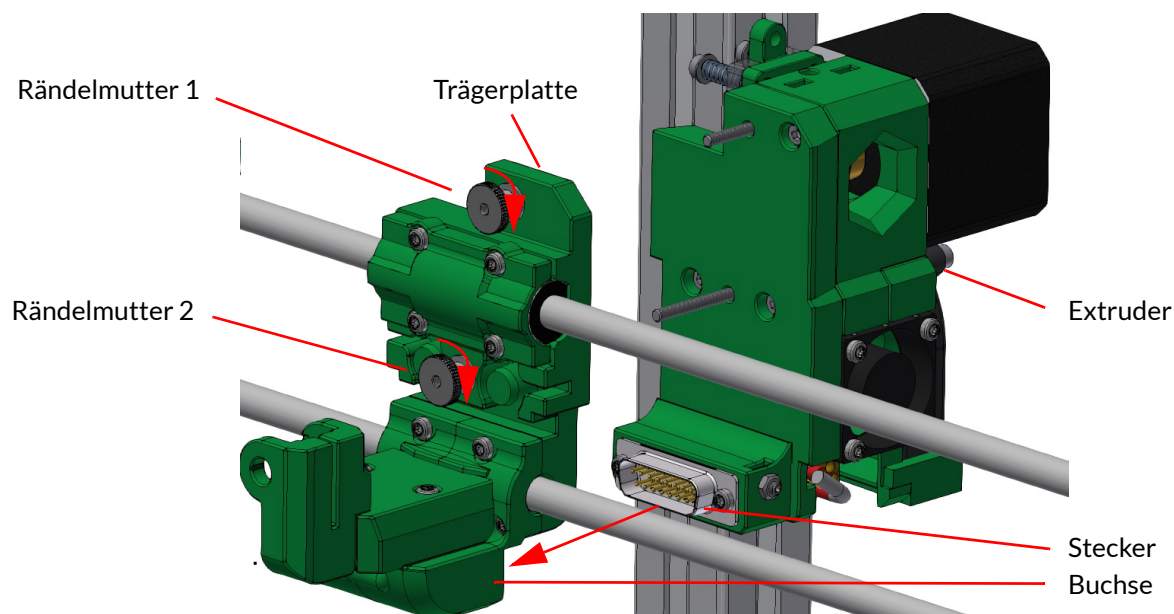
Wechselextruder: Ansicht von hinten, Extruder Einbau
